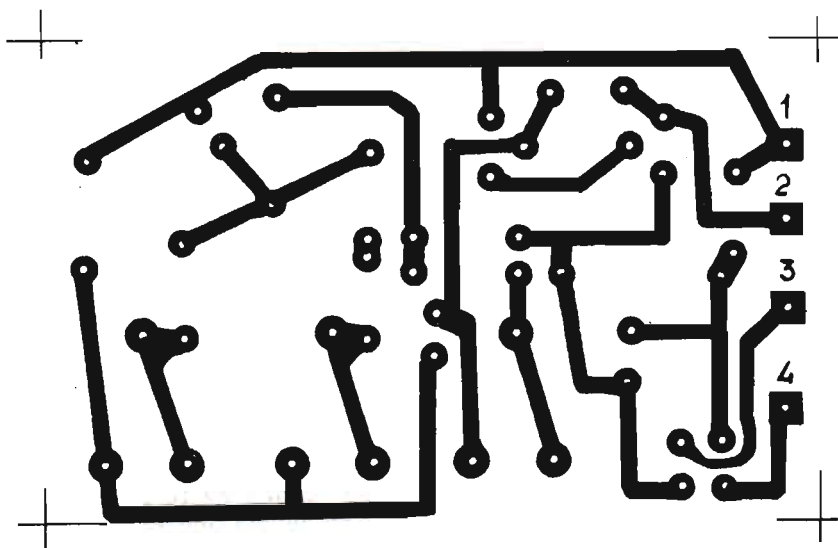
Disegno in grandezza reale del circuito stampato sul quale deve essere composto il modulo elettronico del campanello.
